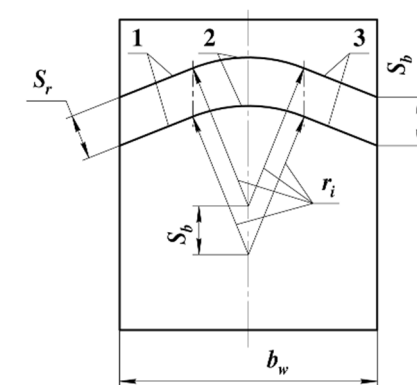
Развертка двух винтовых линий с основного цилиндра на плоскость зацепления:
